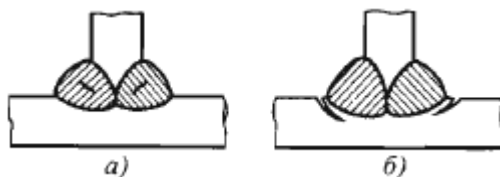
Трещины в сварных соединениях и швах: а - в наплавленном металле; б - в зонах сплавления и термического влияния.
